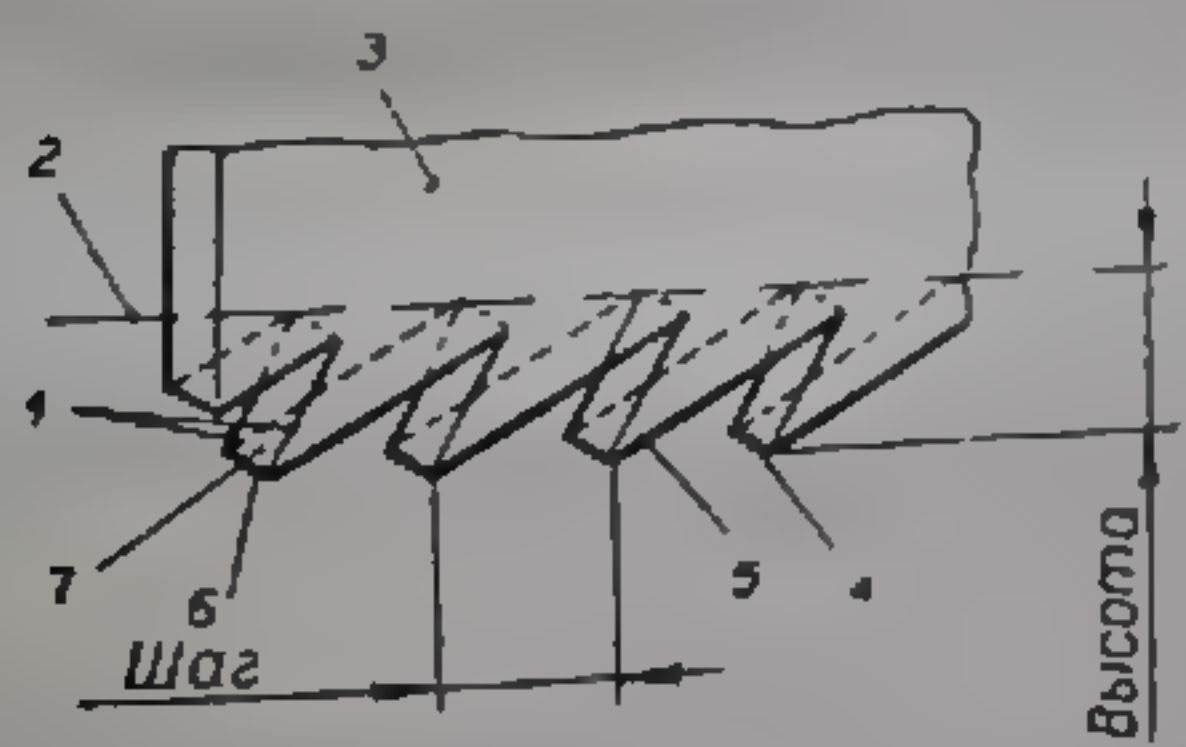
Элементы полотна пилы: 1 — боковые режущие кромки; 2 — линия основания зубьев; 3 — полотно; 4 — вершина зуба; 5 — пазуха; 6 — передняя короткая режущая кромка; 7 — передняя грань.
